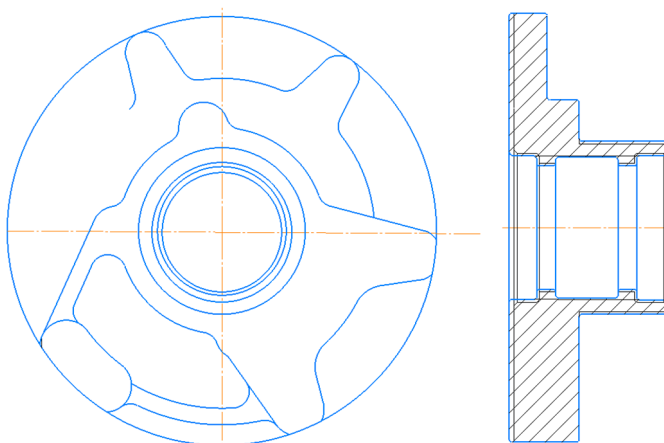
Ескіз деталі «Стакан підшипниковий»
